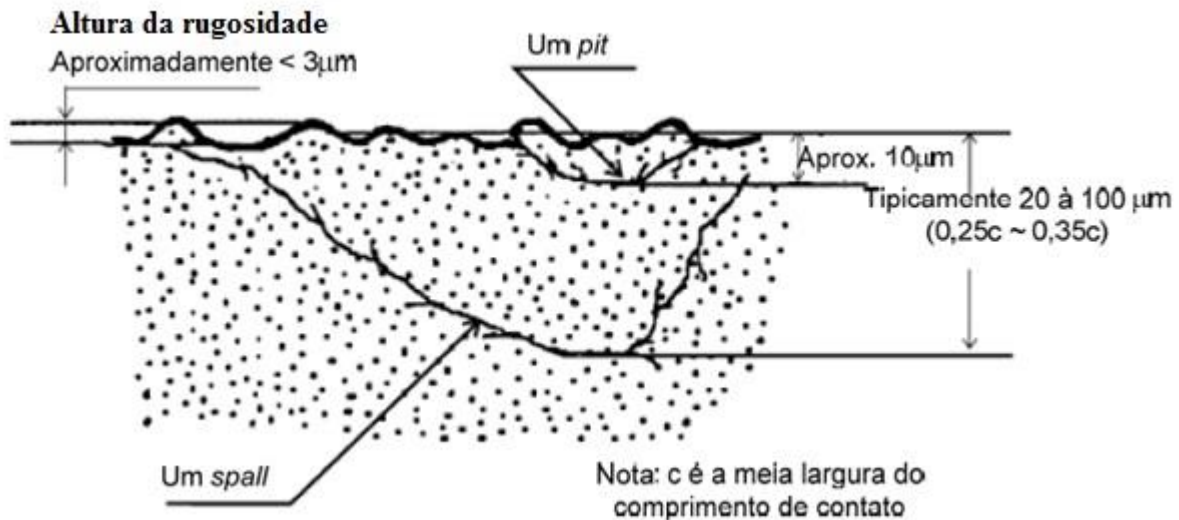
Ilustração esquemática do fenômeno de pitting e spalling [5]
